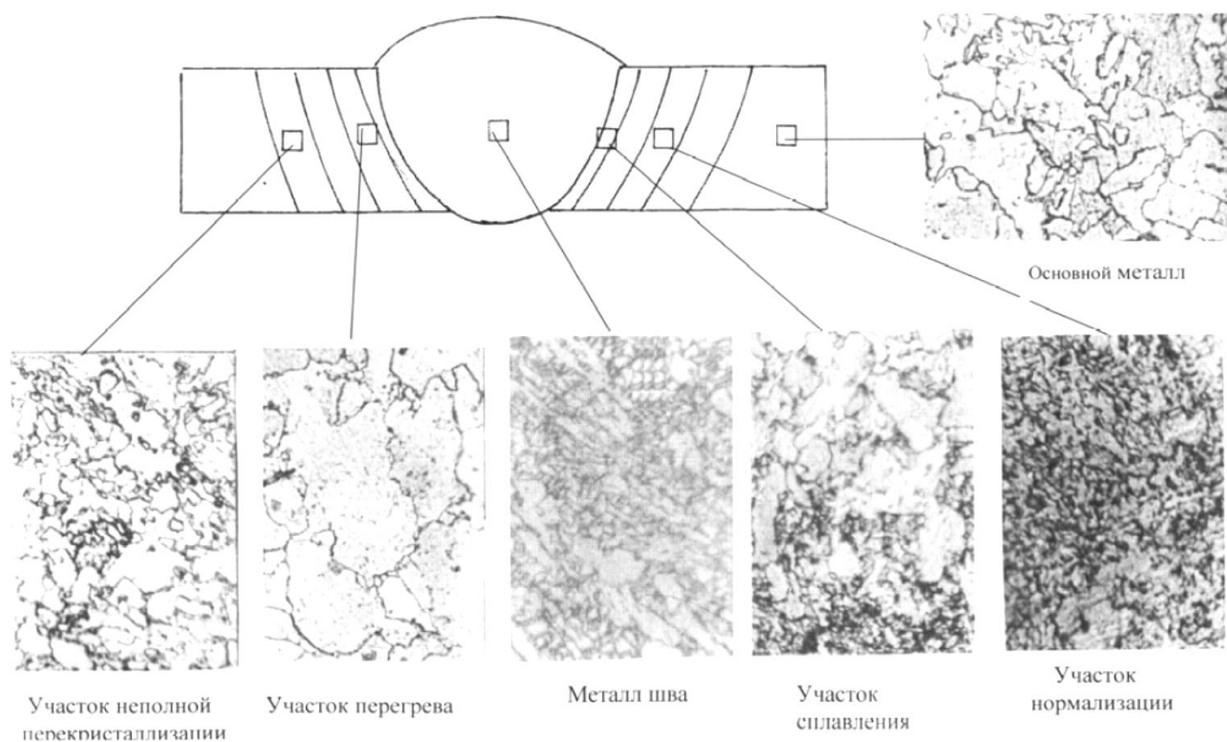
Микроструктура шва при ручной дуговой сварке стали 15ХМ
